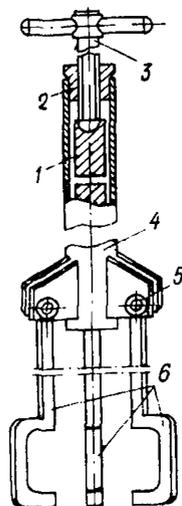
Приспособление для снятия рабочего колеса с вала центробежных насосов типа НДиД
